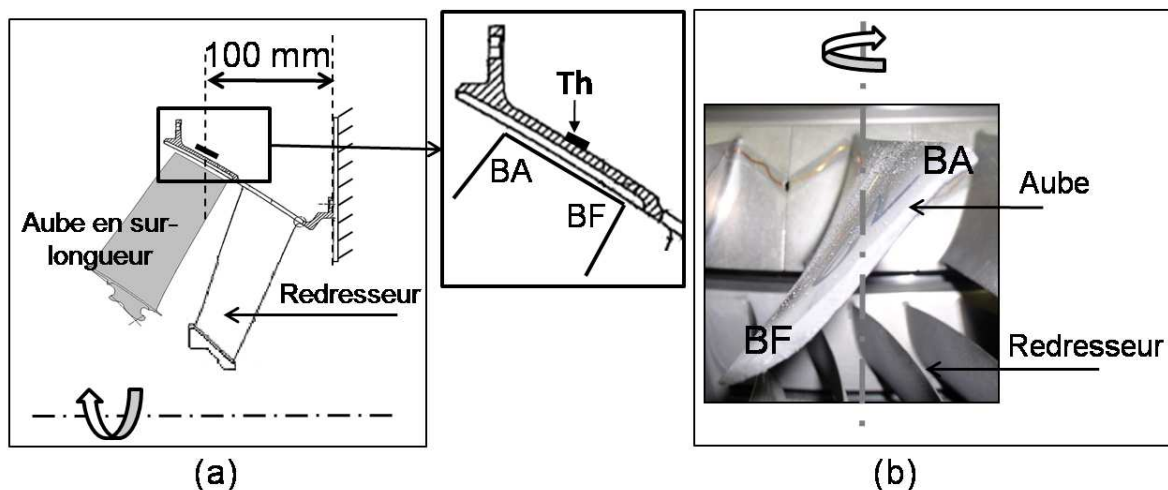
(a) vue en coupe de l'étage du compresseur testé. Th désigne la position axiale des thermocouples (et accéléromètres) du carter. (b) définition du bord d'attaque (BA) et du bord de fuite (BF) de l'aube vue de dessus.
